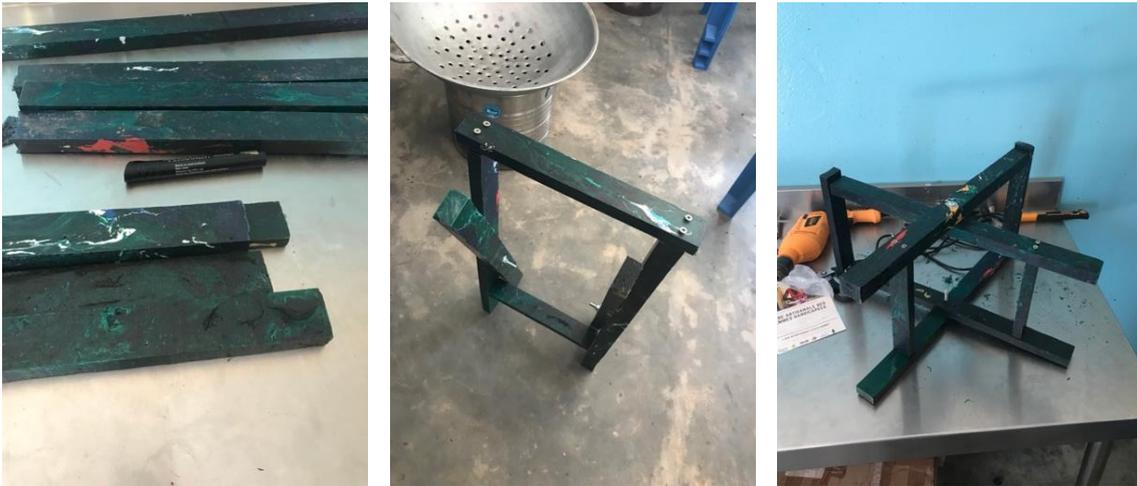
PROCESO DE ENSAMBLAJE DEL TABURETE PLEGABLE. FUENTE: PROPIA
